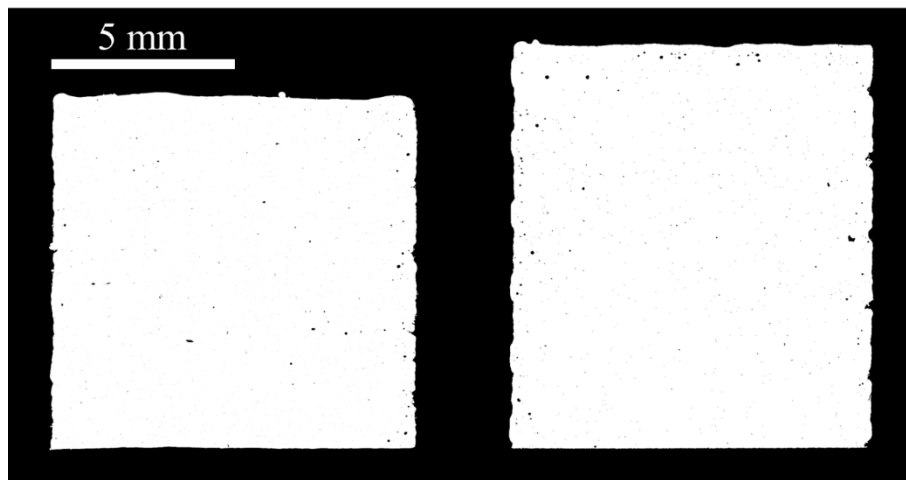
Schliffbild der Probe mit der höchsten relativen Dichte von 99,84 % (links, vs: 800 mm/s, hs: 0,1 mm) und der Probe, die mit dem für die Probenfertigung ausgewählten Parametersatz gefertigt wurde (rechts, vs: 1400 mm/s, hs: 0,09 mm)
